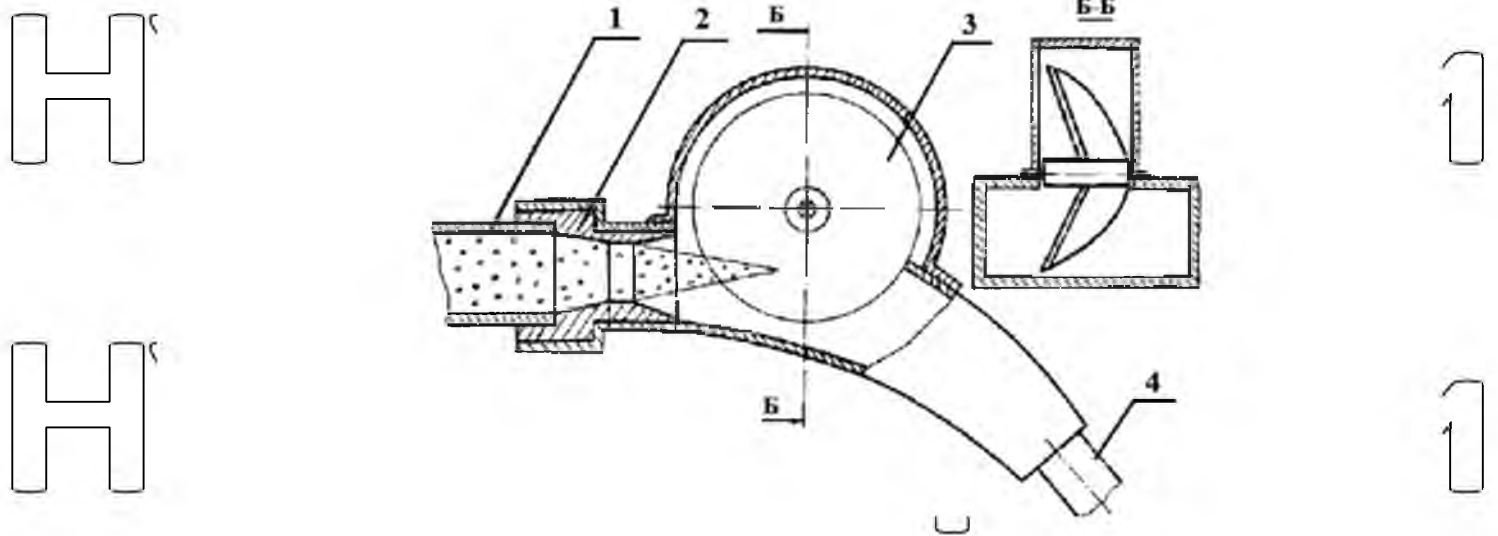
Схема дистриб'ютора з робочим колесом:
